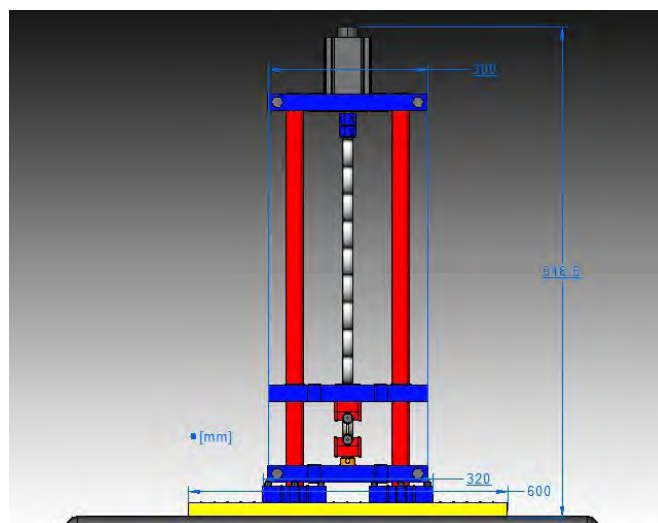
Vista frontal, dimensiones del Probador Mecánico.
